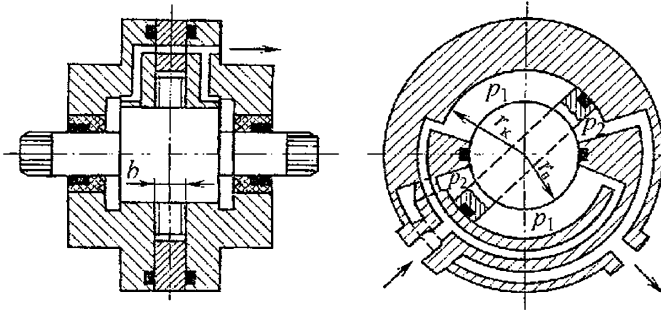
Поворотный гидродвигатель с двумя лопастями
